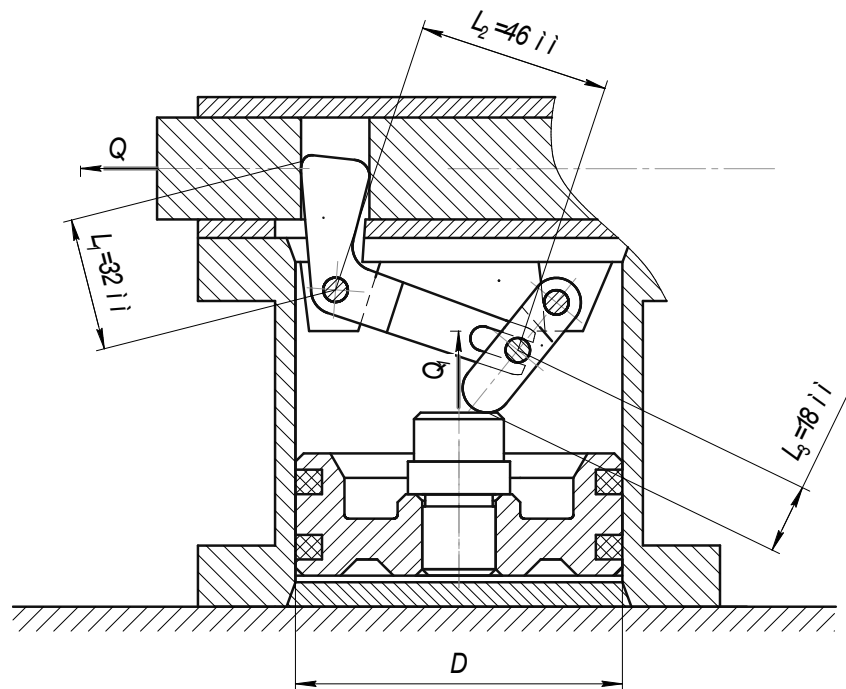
Розмірна схема при закріпленні заготовки
